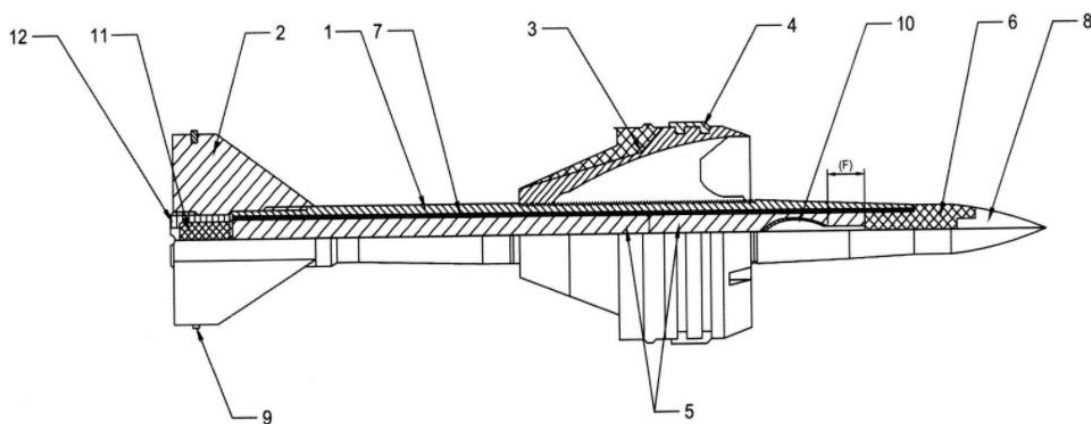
Бронебойный оперенный подкалиберный снаряд : 1 - корпус снаряда, 2 - калиберный стабилизатор, 3 - obturator, 4 - obturiрующий пояс, 5 - первый и второй сердечники, 6 - демпфер, 7 - рубашка из легкоплавкого сплава, 8 - баллистический наконечник, 9- центрирующие штифты, 10 - эллипсоидная полость облицованная пластичным материалом (медь), 11 - трассер, 12 - гайка трассера
